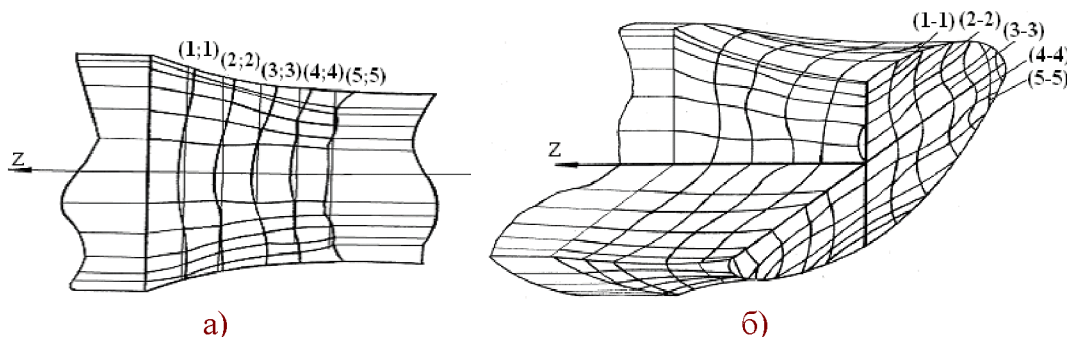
Переміщення координатної сітки: а – на боковій поверхні; б – по об'єму вальцьованої заготовки:
